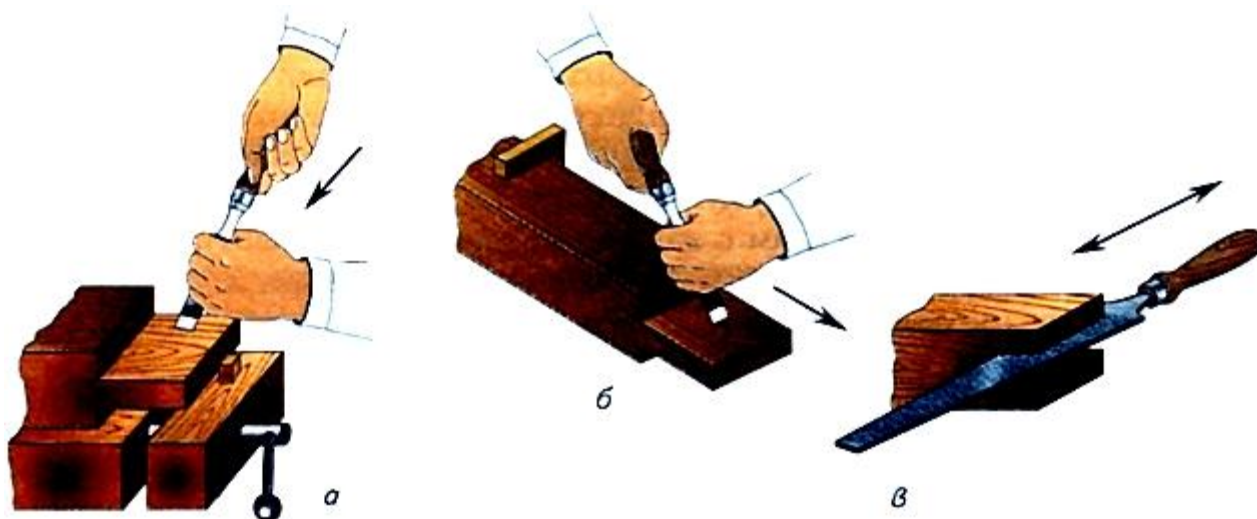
Обработка шипов и проушин в размер: а, б — стамеской; в — напильником
